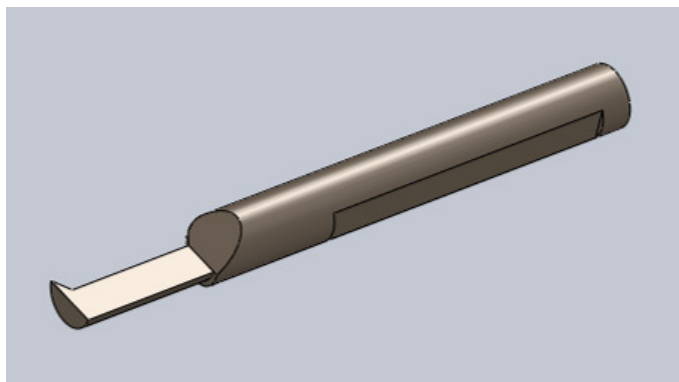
Innendrehwerkzeug 8mm bis 16mm
